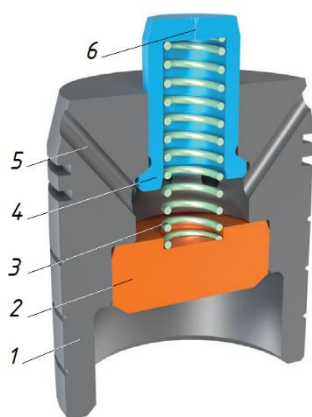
Гідравлічний поршень механізму приводу випускного клапану дизелів серії MC та MC-C фірми MAN: 1 – гідравлічний поршень приводу клапану; 2 – регулювальна проставка; 3 – пружина; 4 – демпферний поршень; 5 – канал сполучення підпоршневої та надпоршневої порожнини; 6 – дросельний отвір [10]
